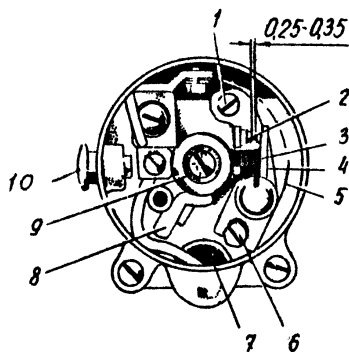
Магнето: 1 - гвинт; 2 - нерухомий контакт; 3 - рухомий контакт; 4 - стояк; 5 - пружина рухомого контакту; 6 - ексцентрик; 7 - конденсатор; 8 – фільтр для змащування кулачка; 9 - кулачок переривника; 10 - кнопка ручного вимикання запалювання
